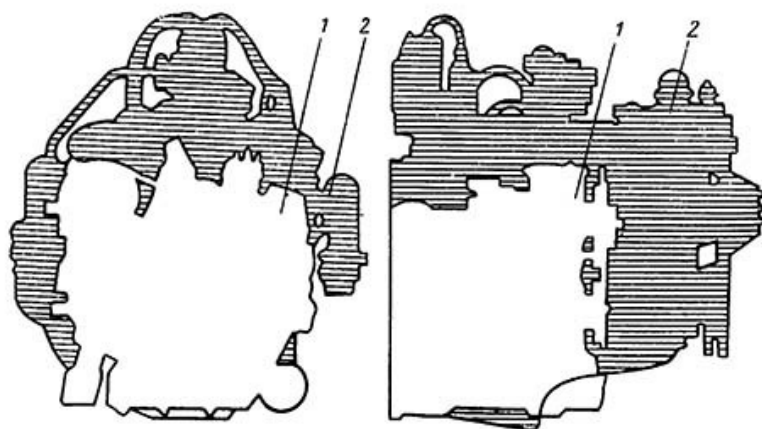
Сопоставление габаритов РПД и V-образного восьмицилиндрового поршневого двигателя:
